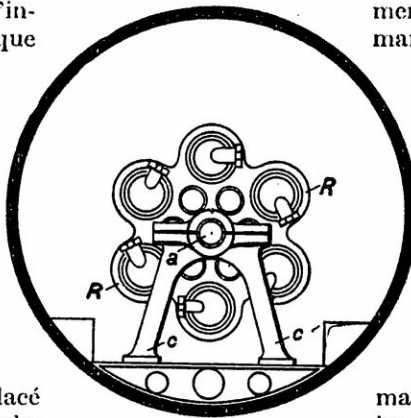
VUE DE L'ARRIÈRE DU MAGASIN A TORPILLES
